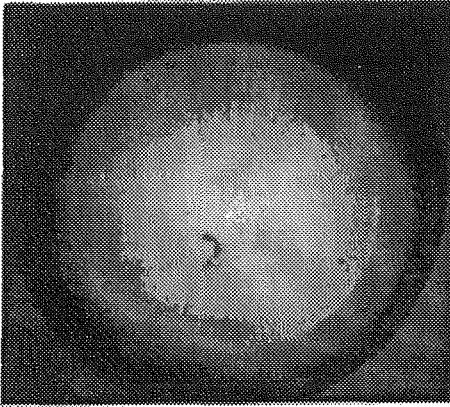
PONTO DE SOLDA PERFEITO
